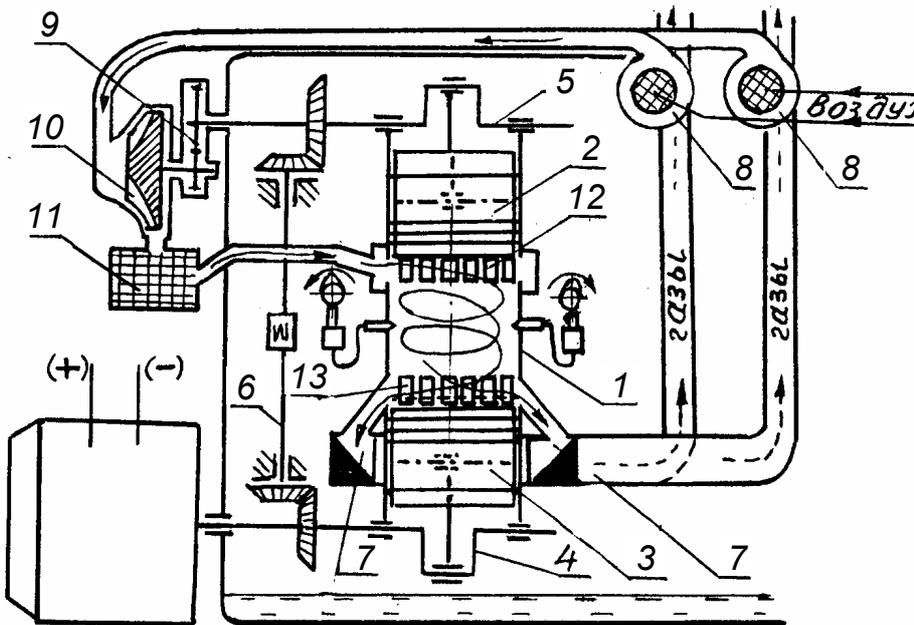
Двухтактный дизель с прямооточной продувкой цилиндров: 1 – блок цилиндров; 2 – поршень верхний; 3 – поршень нижний; 4 – вал нижний; 5 – вал верхний; 6 – вал промежуточный; 7 – выпускные коллекторы; 8 – турбокомпрессоры; 9 – редуктор; 10 – нагнетатель второй ступени сжатия; 11 – воздухоохладитель; 12 – окна продувочные; 13 – окна выпускные
